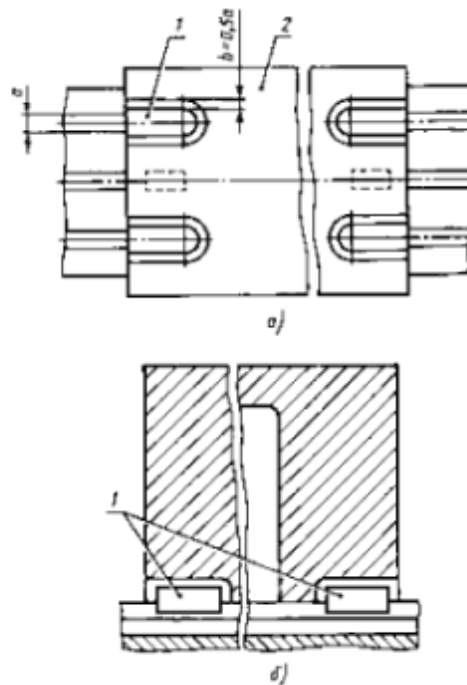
Базирование корпуса приспособления на столе станка:
